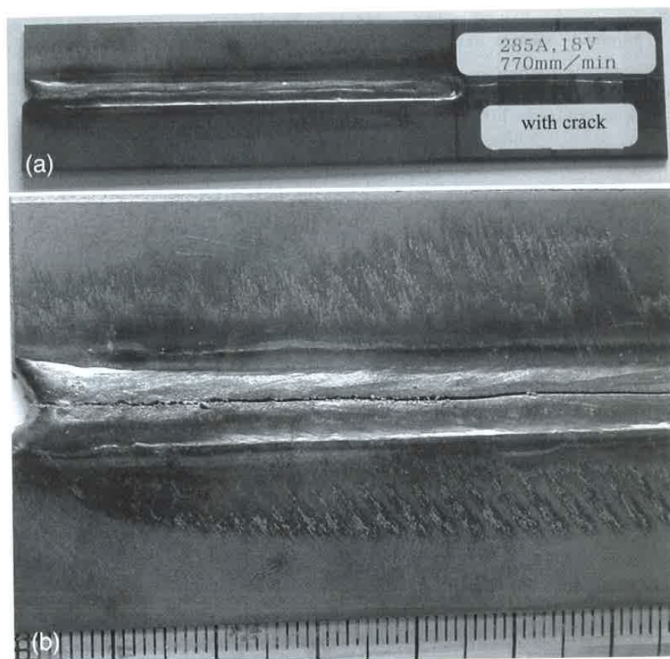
Éprouvette fissurée après un essai JWRI : (a) vue d'ensemble d'éprouvette ; (b) vue sur la partie fissurée de l'éprouvette [SSM01]
